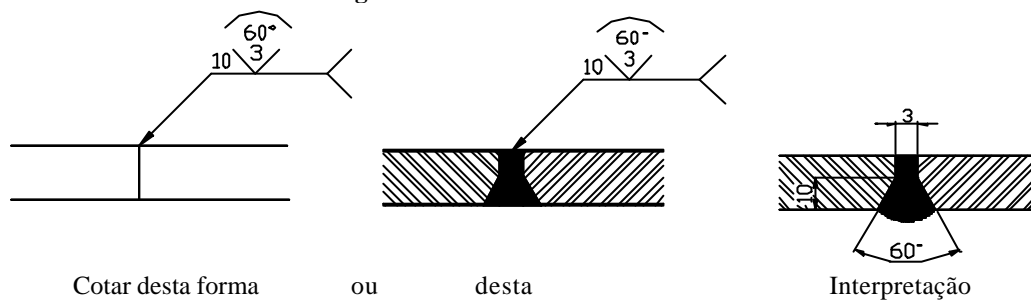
Junta soldada com reforço de solda
